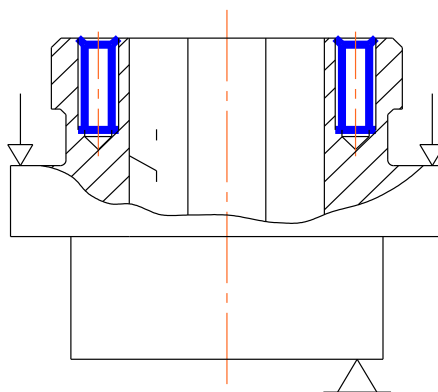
Умовна схема базування на свердлильній операції.
